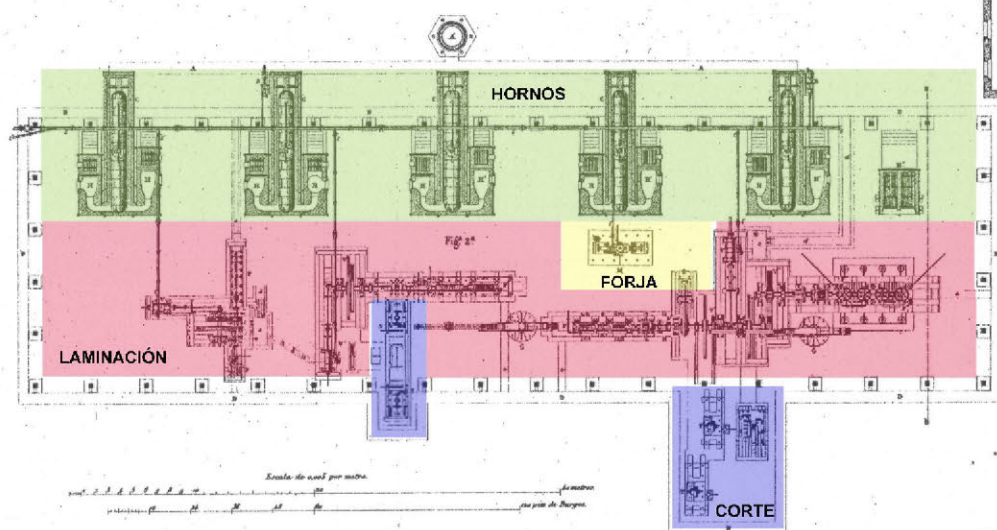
Plano de Implantación. Obsérvese las secciones: hornos, forja, laminación y corte.
